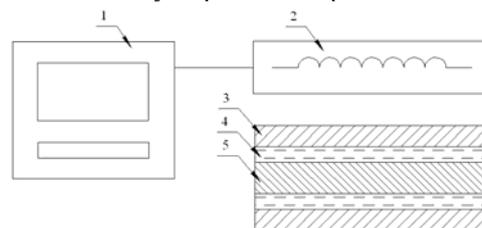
Схема индукционного нагрева: 1 – рабочая станция, 2 – индуктор, 3 – цилиндр пластикации, 4 – полимерный материал, 5 – шнек
